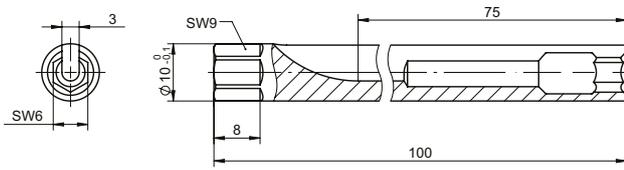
Montagewerkzeug Typ 1300A165, SW9 ... SW6
